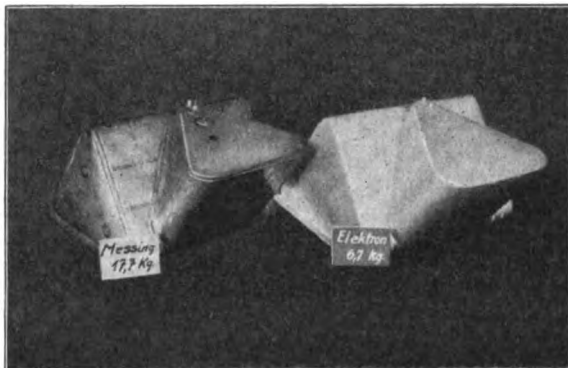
Flügeltank für ein Junkers-Flugzeug F 13 in Elektron verglichen mit der Messingausführung.
